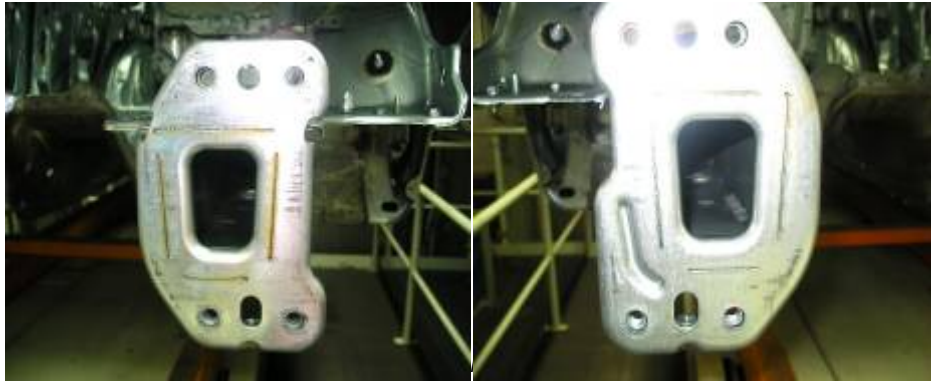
Soldadura realizada en cabinas láser.
